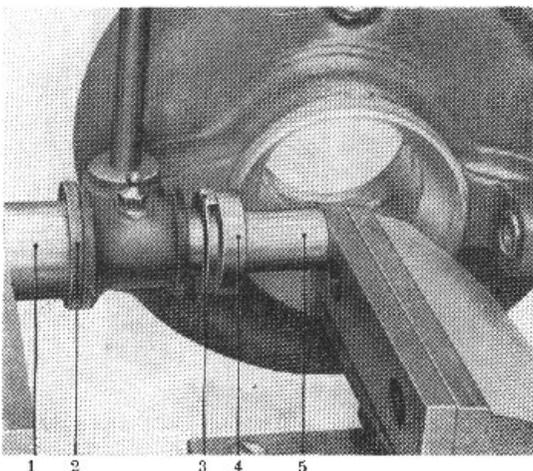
Obere und untere Buchse in Schwenklager eindrücken
